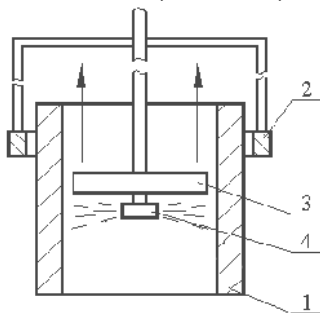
Схема предложенного способа термообработки гильз цилиндров
